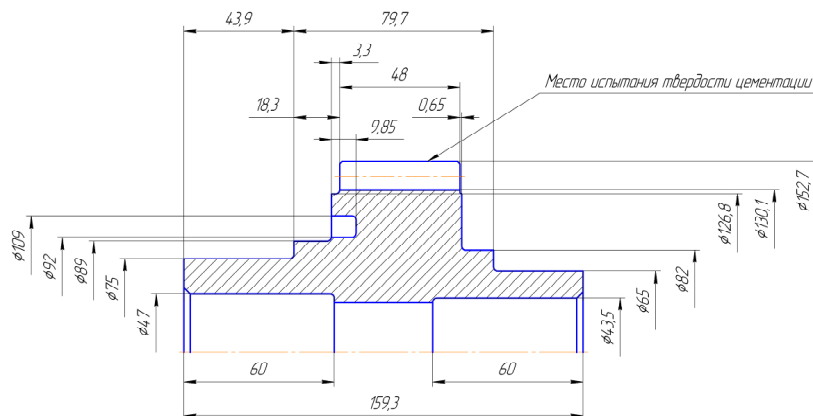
Эскиз обрабатываемой детали типа «колесо зубчатое» из стали 16ХЗНВФМБ-Ш
